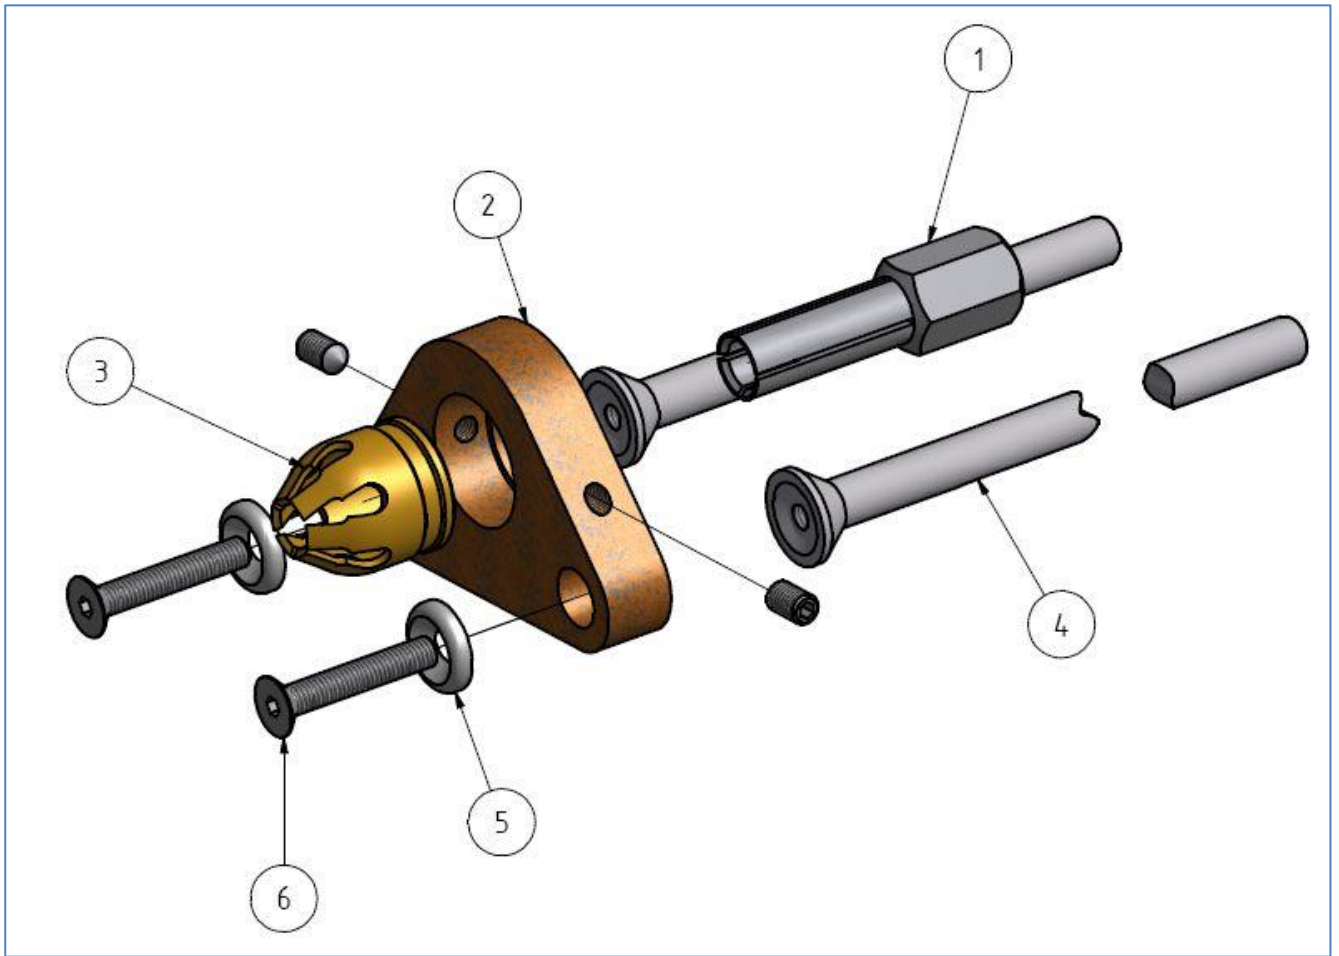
Stützeinrichtung zum Kurzzeitbolzenschweißen ohne Schutzgas
